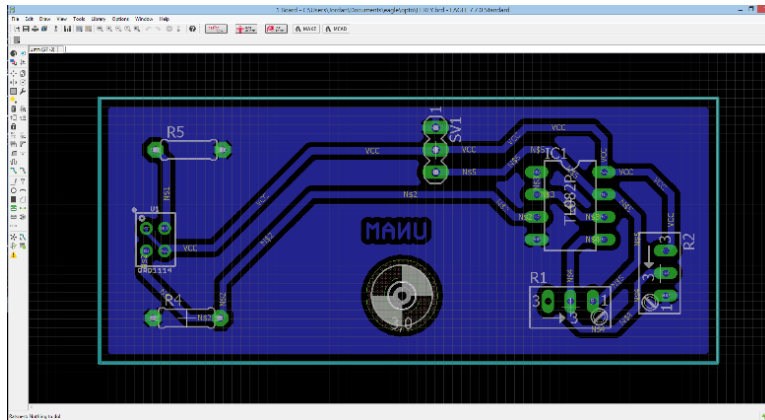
Diseño en PCB de la tarjeta de acondicionamiento y disparo.
